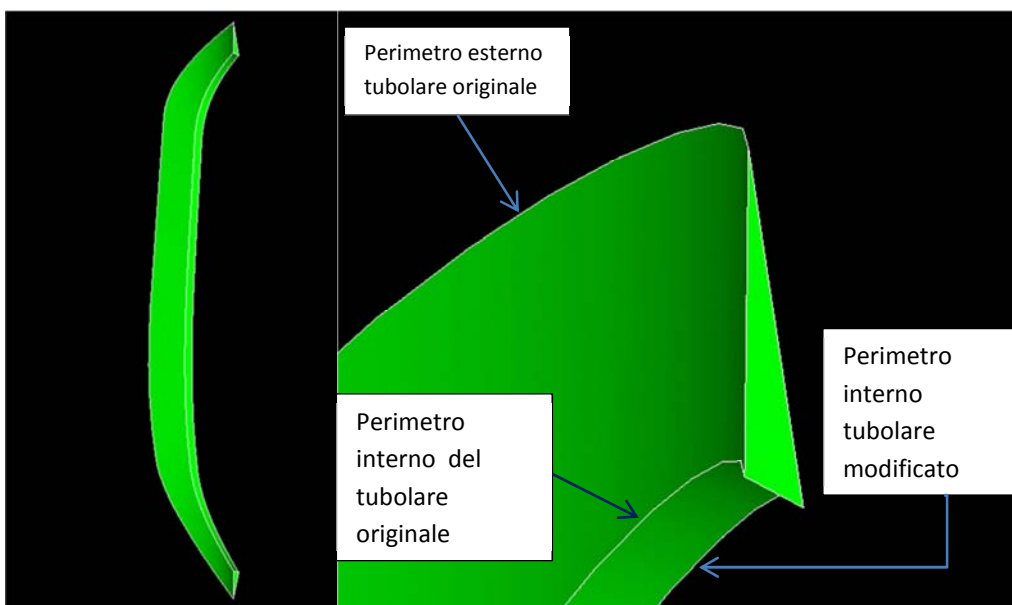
Volume del cuneo da rimuovere dal tubolare originale a) volume sezionato, b) particolare area sezione.
